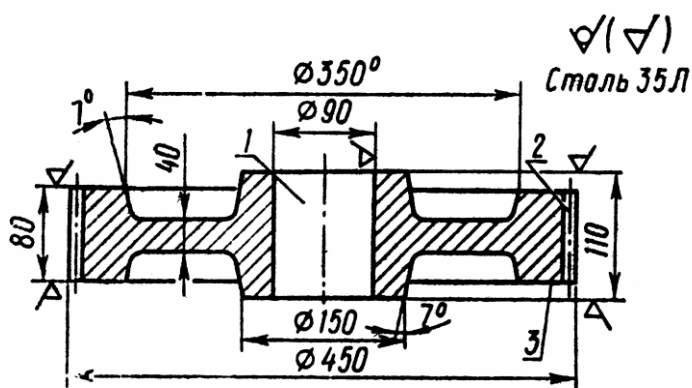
Зубчатое колесо. Сталь 35Л.
